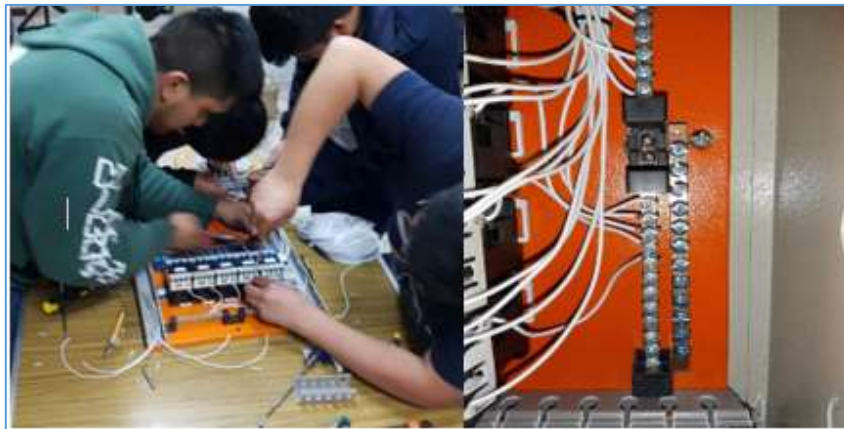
Implementación de cableado AC en la estructura interna del tablero
